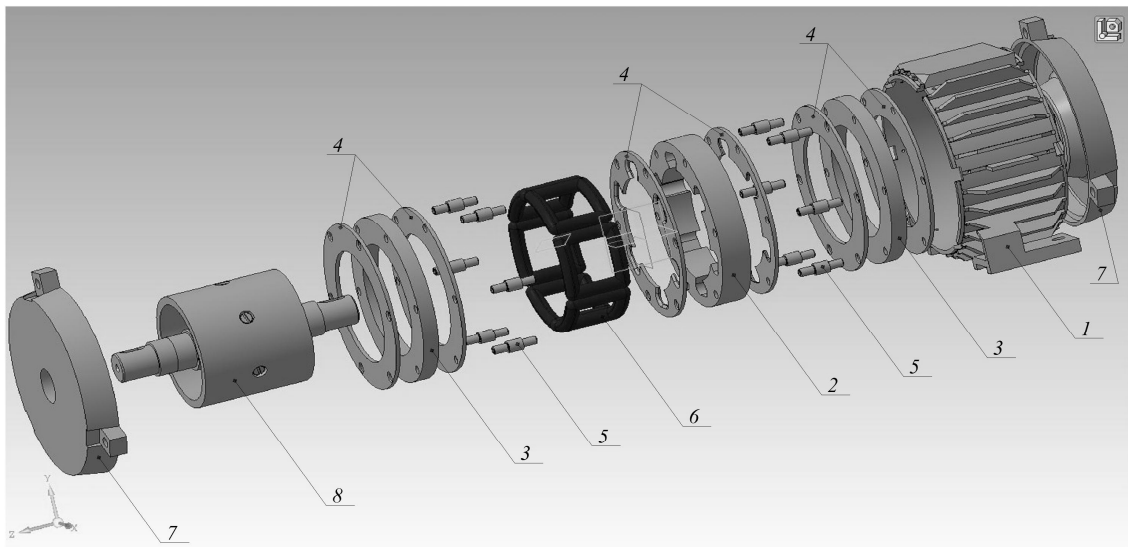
Рознесена 3D модель ДРК-50-6: 1 – станина; 2 – центральний пакет осердя статора; 3 – боковий пакет осердя статора; 4 – натискна шайба; 5 – втулка дистанційна; 6 – котушка обмотки статора; 7 – підшипниковий щит; 8 – ротор
